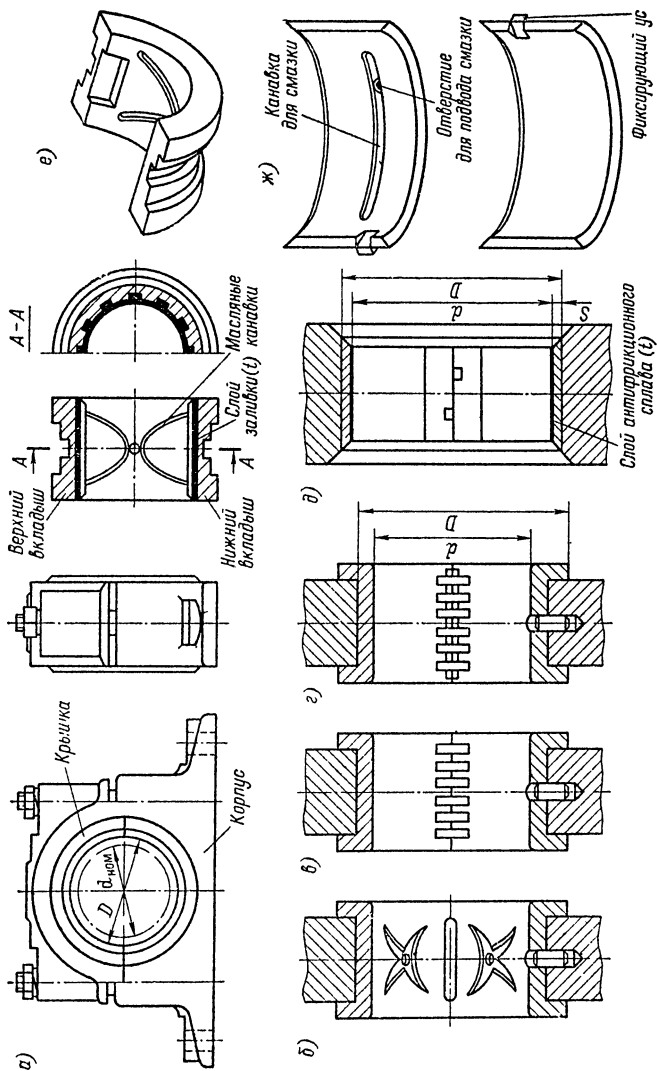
Конструкция разъемных подшипников скольжения: а — основные элементы подшипников; б...г — тонкостенные; д — толкостенные; е — толкостенный вкладыш; ж — тонкостенный вкладыш
